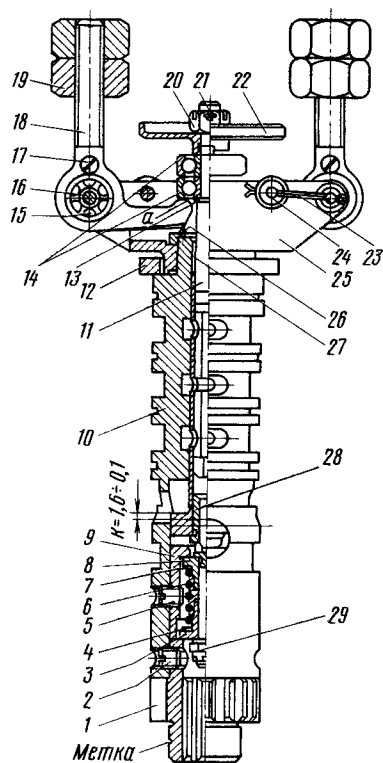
Золотниковая часть все-режимного регулятора дизеля 2Д100: 1 — зубчатое колесо ведущее; 2, 5 — винты стопорные; 3, 8 — тарелки пружины нижняя и верхняя; 4, 7 — шайбы; 6 — компенсирующая пружина; 9 — втулка; 10 — буска золотника; 11 — плунжер; 12 — фланец; 13 — регулировочная шайба; 14, 15 — шарикоподшипники; 16 — ось; 17 — винт; 18 — рычаг грузов; 19 — груз; 20 — гайка золотника; 21, 23 — шпильты; 22 — тарелка все-режимной пружины; 24 — ограничитель; 25 — траверса; 26 — кольцо; 27 — золотник; 28 — хвостовик золотника; 29 — гайка золотника
